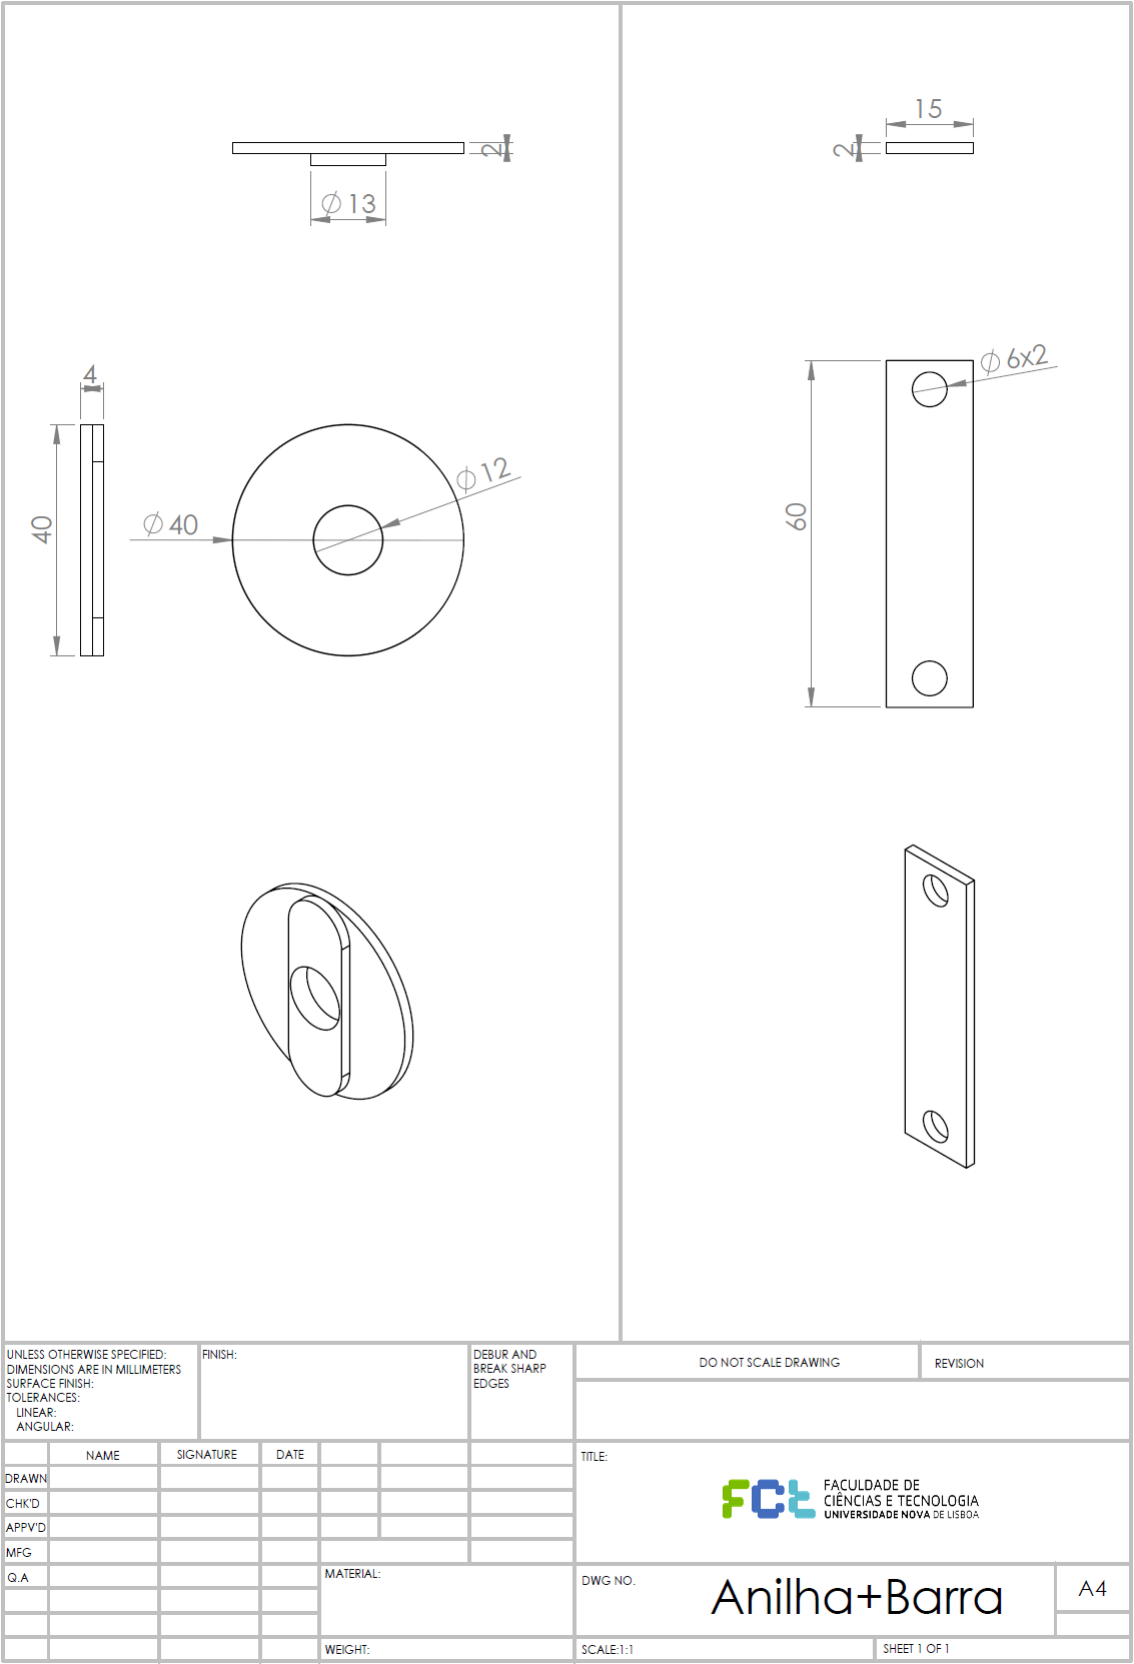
Desenhos técnicos de anilha e barra de fixação da tocha de soldadura
